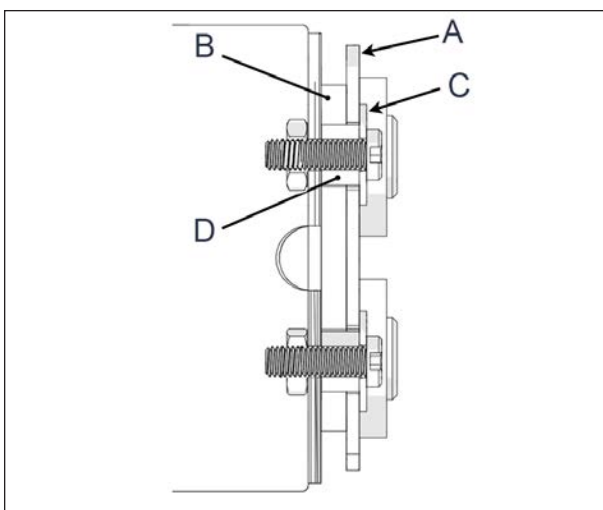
COUPE DE L'ASSEMBLAGE DE LA PLAQUE DE FIXATION LONGUE I À C
